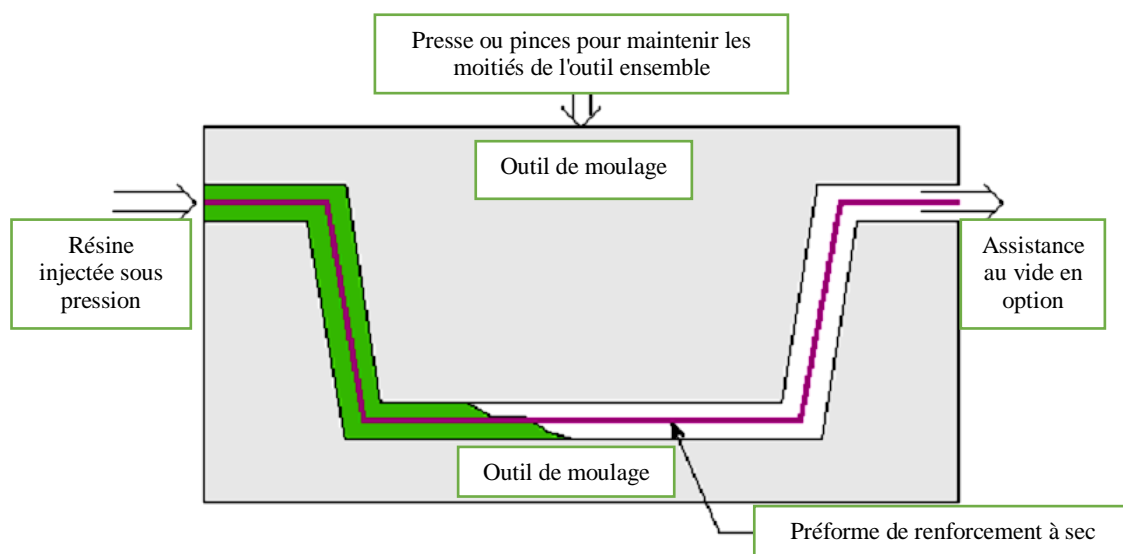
Figure illustrant le moulage par injection de résine [42].
